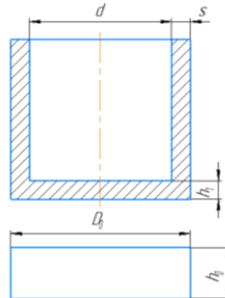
Размеры заготовки и детали при обратном выдавливании
